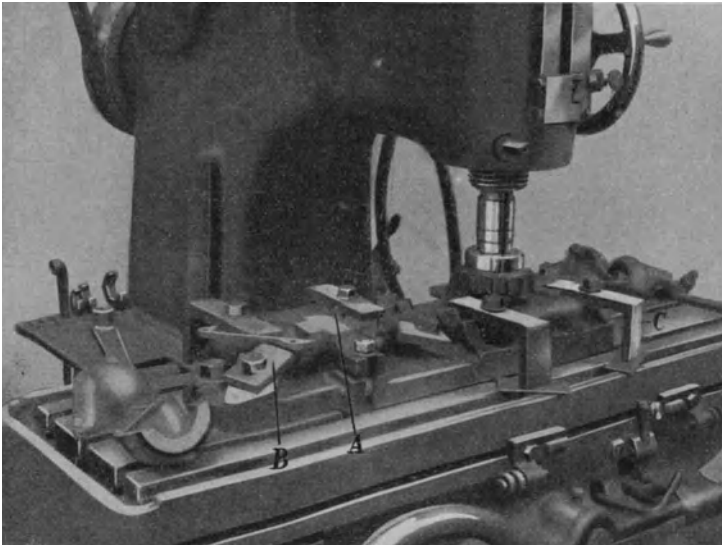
Das Fräsen von Schutzhauben zu Abb. 626.
